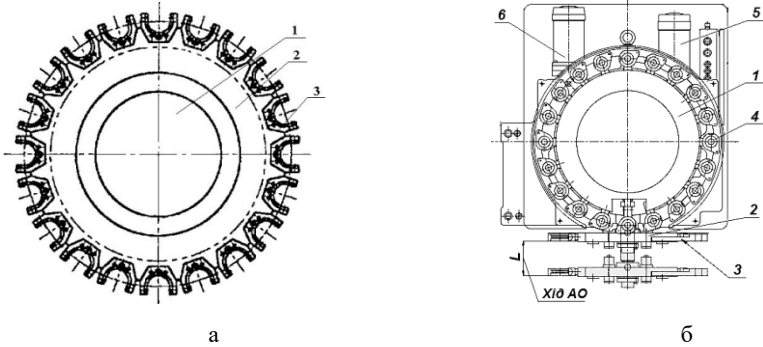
Інструментальні магазини: а – дисковий; б - барабанний
